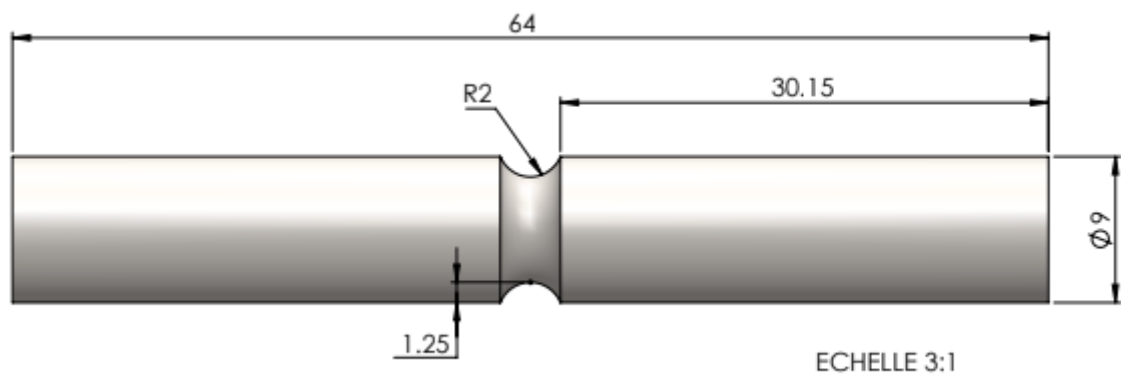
Géométrie et dimension de l'éprouvette U2.
